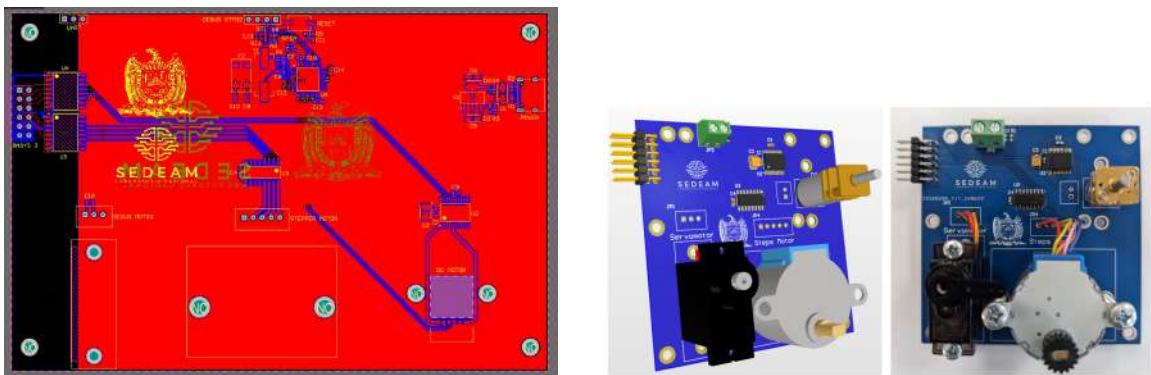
Izquierda: Vista superior del nuevo diseño físico. Derecha: Render 3D de la PCB anterior.
